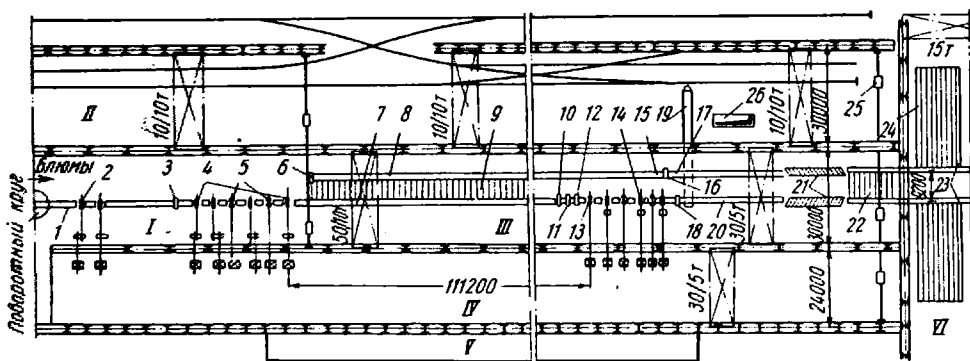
Схема расположения оборудования непрерывного заготовочного стана 900/730/530:
